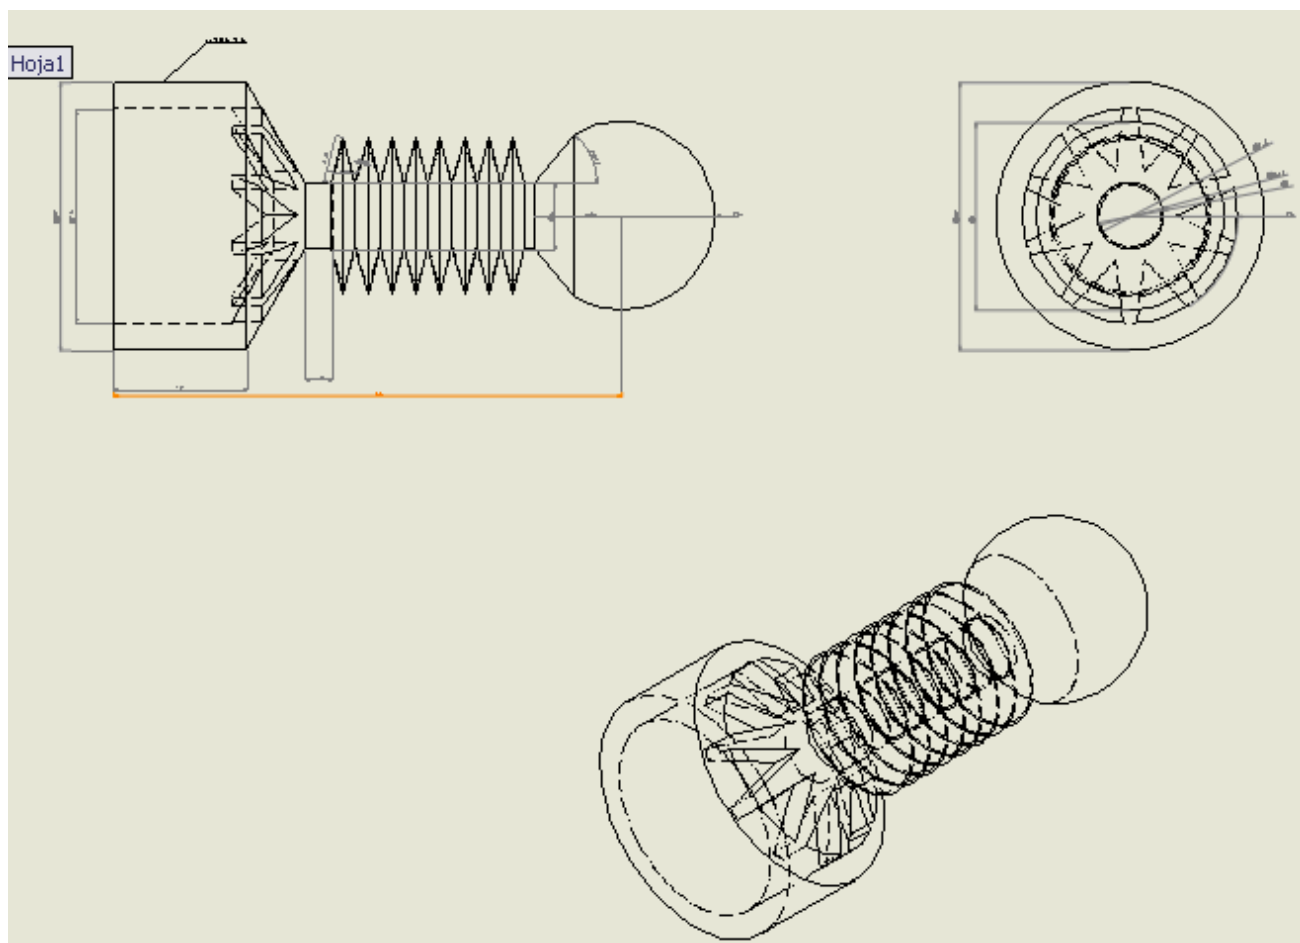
PLANO ELEMENTO EXPANSION
